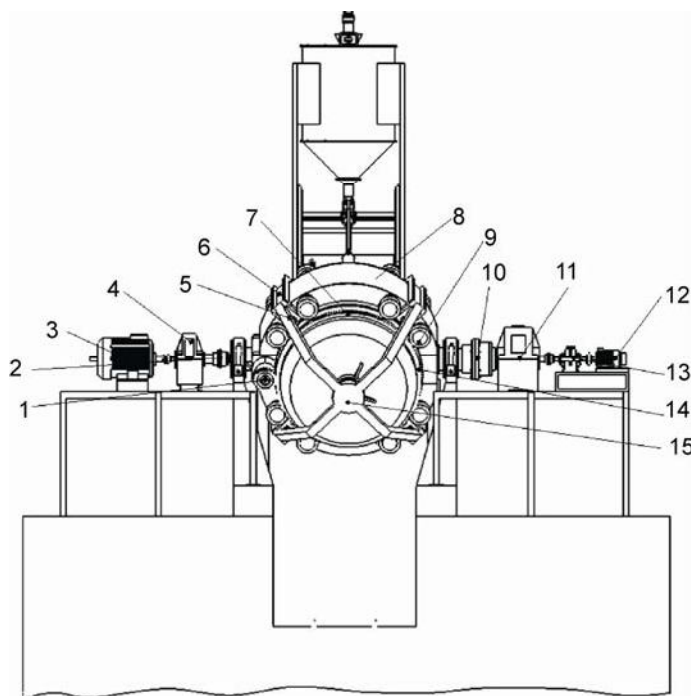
Схема компоновки механизмов наклона и поворота 10-т кислородного конвертера конструкции ДонНТУ
